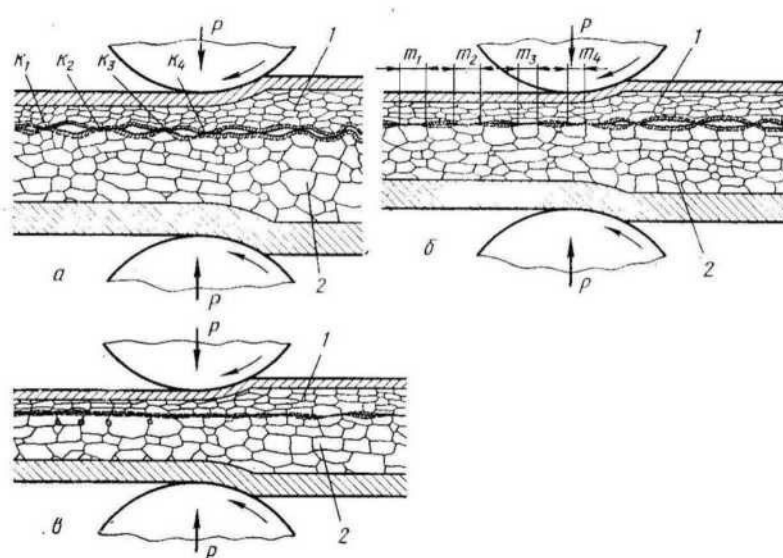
Схема з'єднання між шарами при зварюванні пакета гарячої прокаткою:
